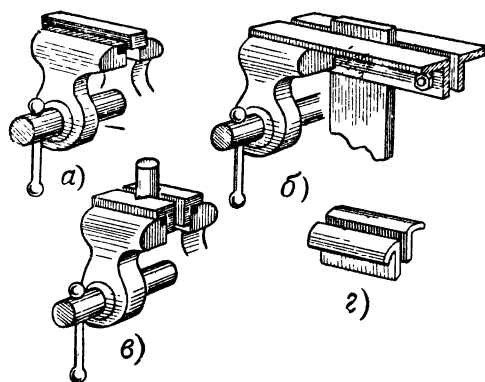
Закрепление заготовок в параллельных тисках.
